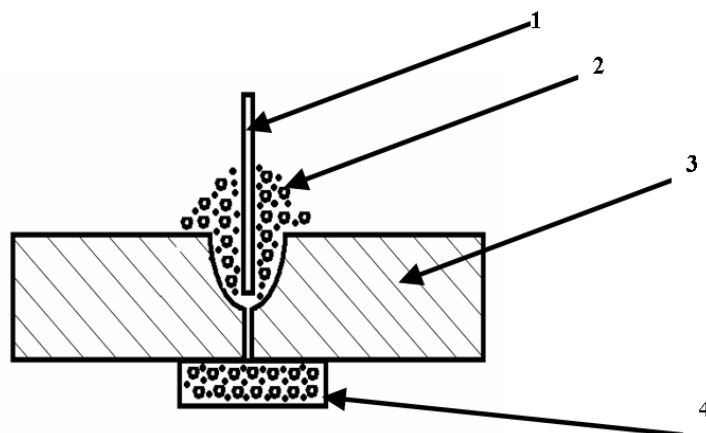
Принципиальная схема процесса однопроходной сварки медной гильзы кристаллизатора: 1 – сварочная проволока; 2 – сварочный флюс; 3 – свариваемая медная заготовка со специальной U – образной разделкой кромок; 4 – флюсовая подушка
